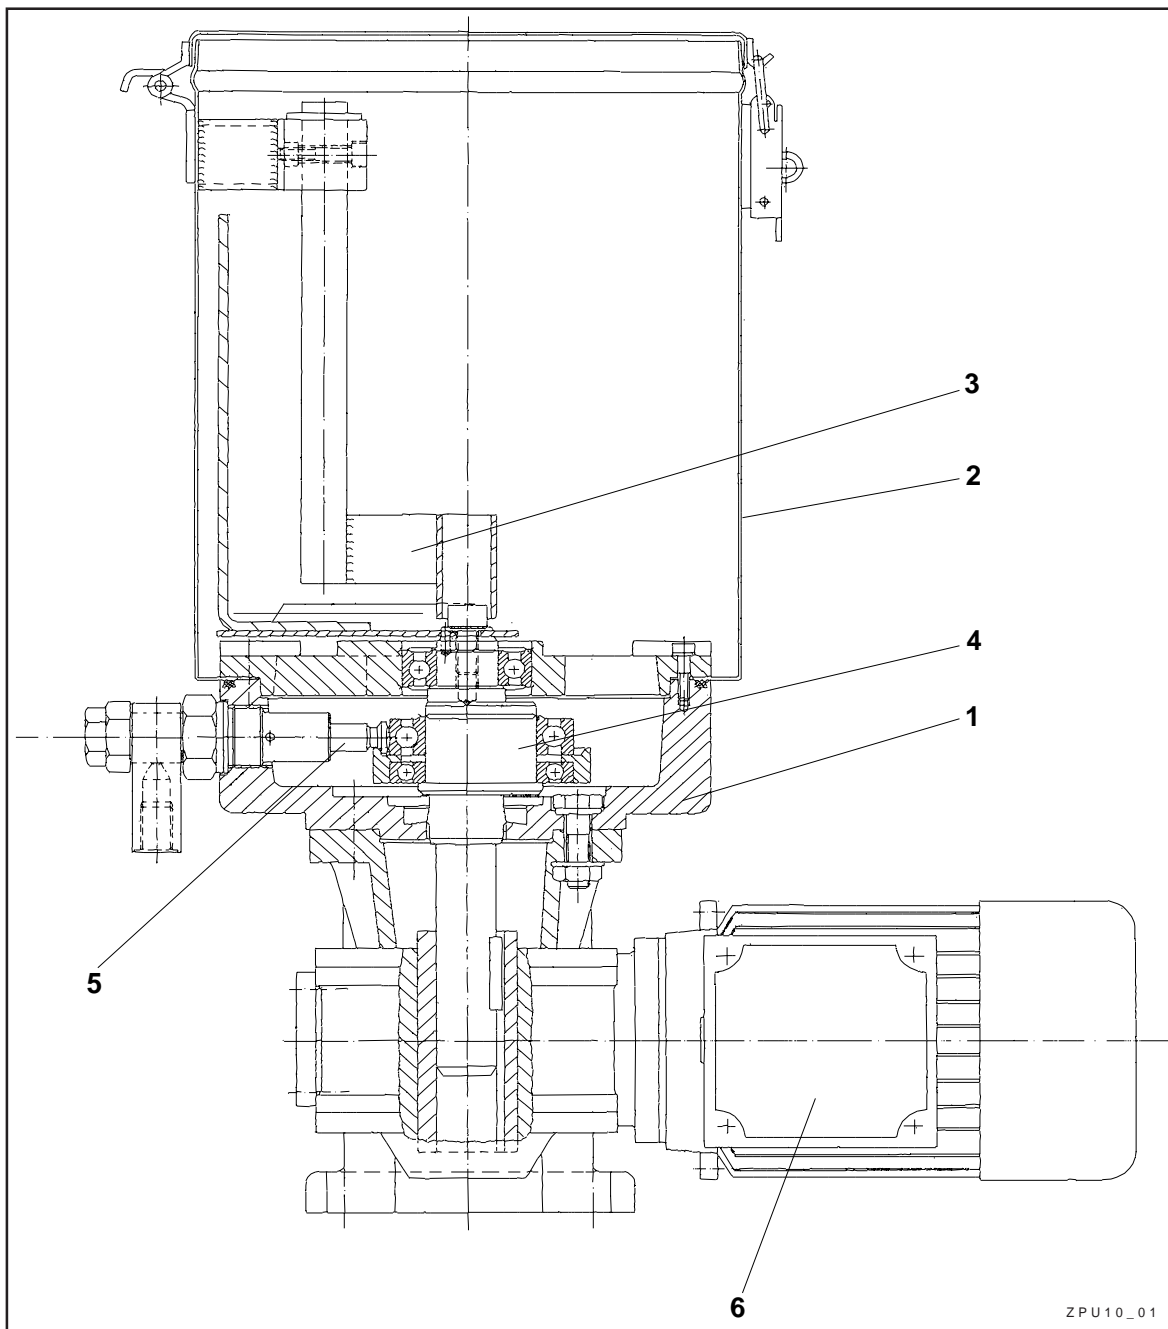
Dibujo seccional de la bomba ZPU 01/02
